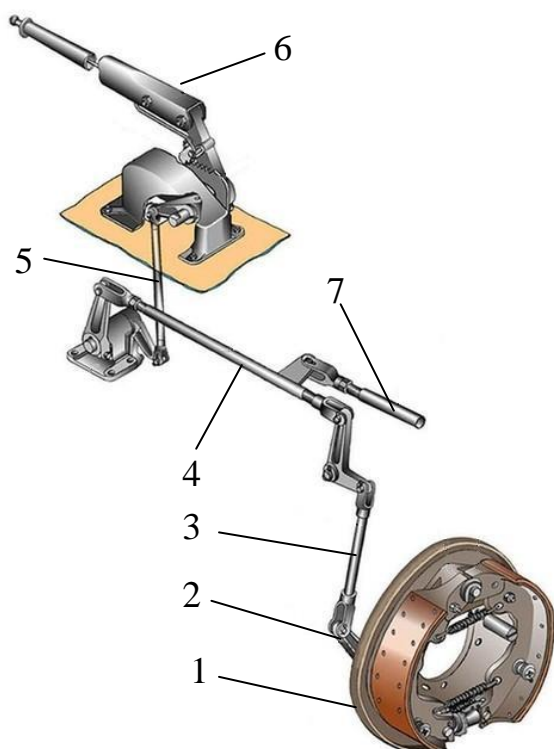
Механический привод трансмиссионного стояночного тормоза автомобиля УРАЛ: 1 – трансмиссионный барабанный тормозной механизм; 2 – рычаг привода разжимного механизма; 3, 4, 5 – тяги; 6 – рычаг управления стояночным тормозом; 7 – тяга привода тормозного крана прицепа
